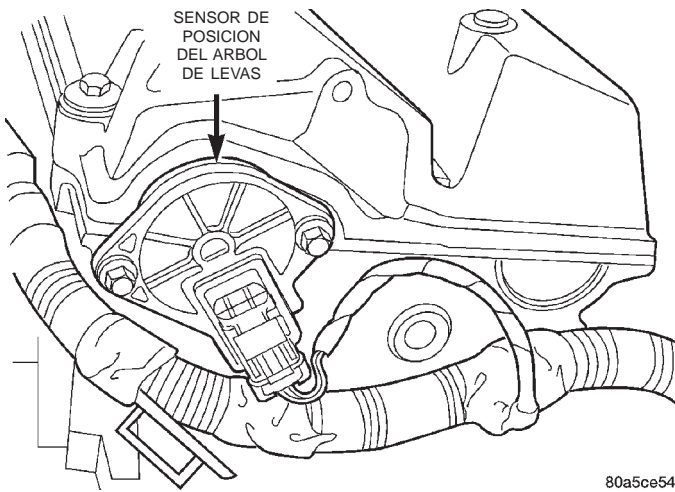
Sensor de posición del árbol de levas—Motor 2.4L DOHC (doble árbol de levas a la cabeza)
